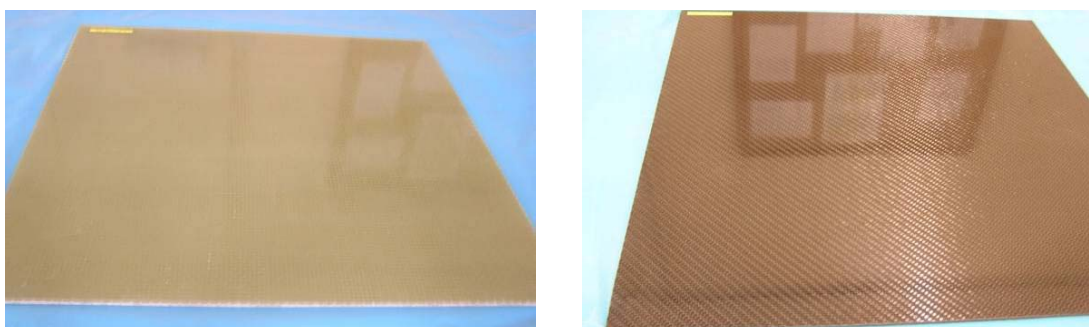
Plaque démoulée et découpée après l'infusion.
